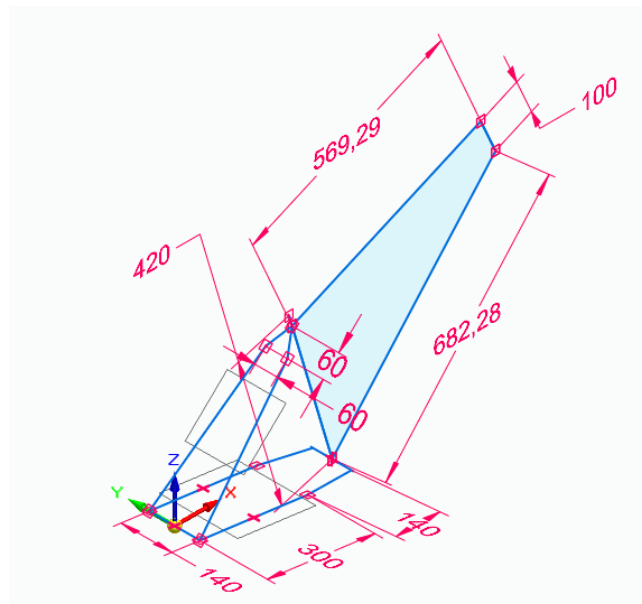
Esboço 3D das dimensões macro do quadro
